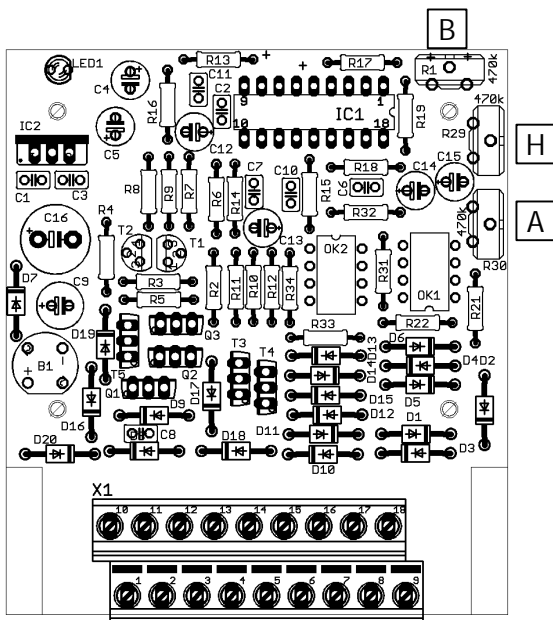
Anschlussplan – Connections – Plan de connexion - Aansluitplan
